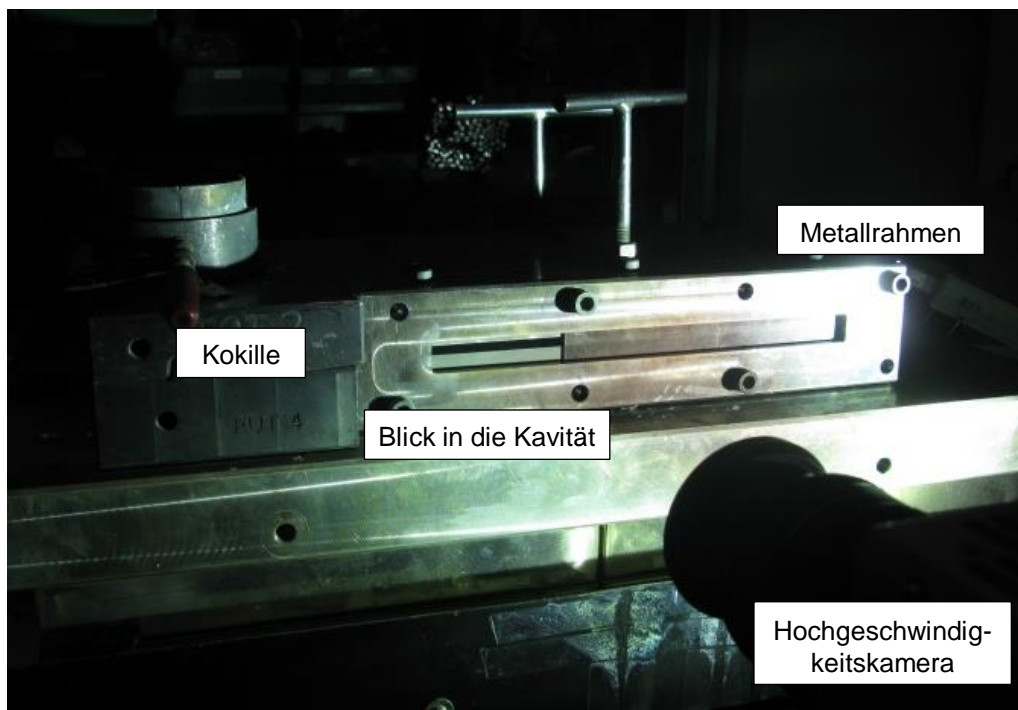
Versuchsaufbau für die Hochgeschwindigkeitsaufnahmen mit Frontallicht
